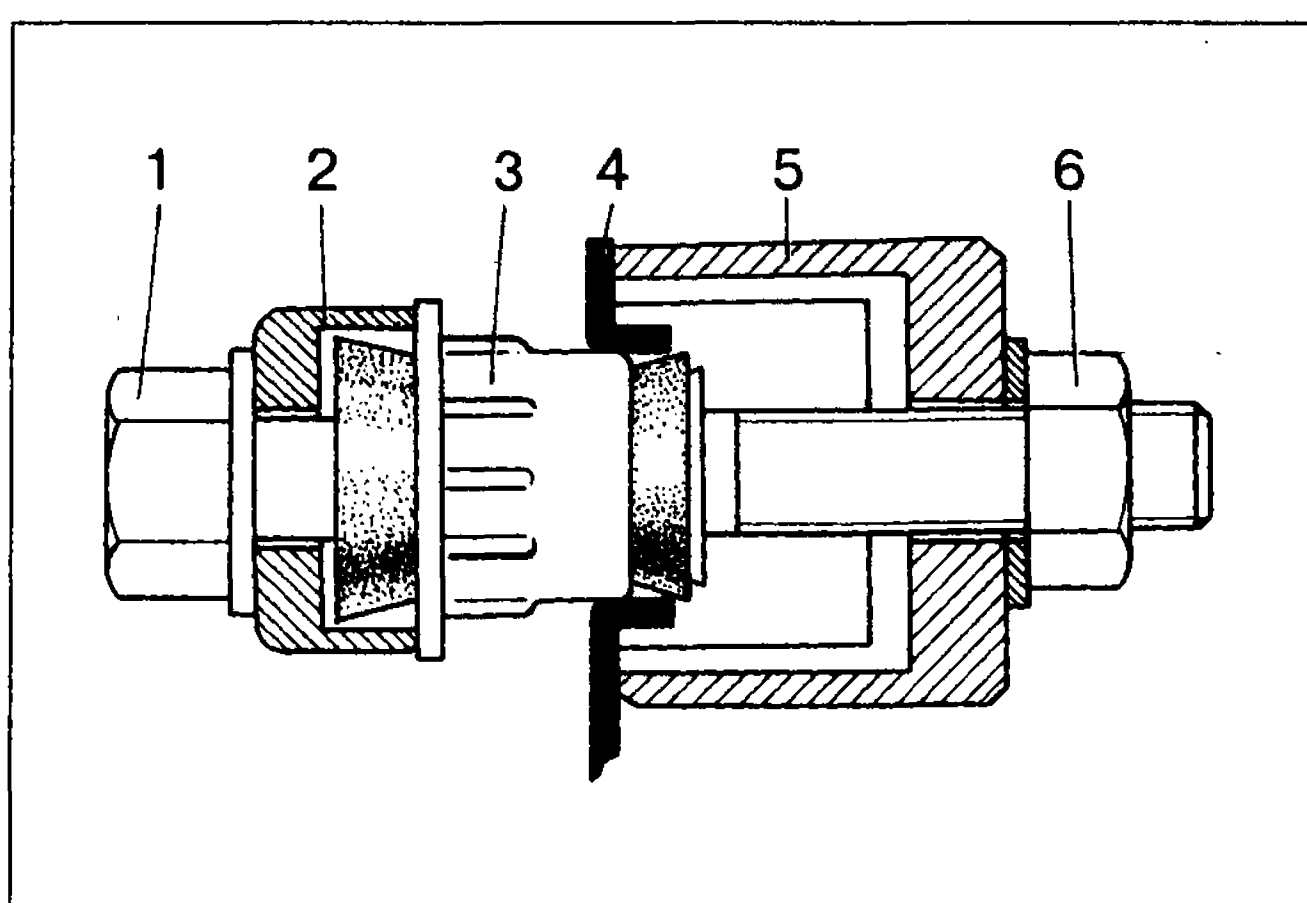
Схема запрессовки шарнира верхнего рычага: 1-болт; 2-кольцо приспособления А.47046; 3-шарнир; 4-верхний рычаг; 5-стакан приспособления А.47046; 6-гайка
